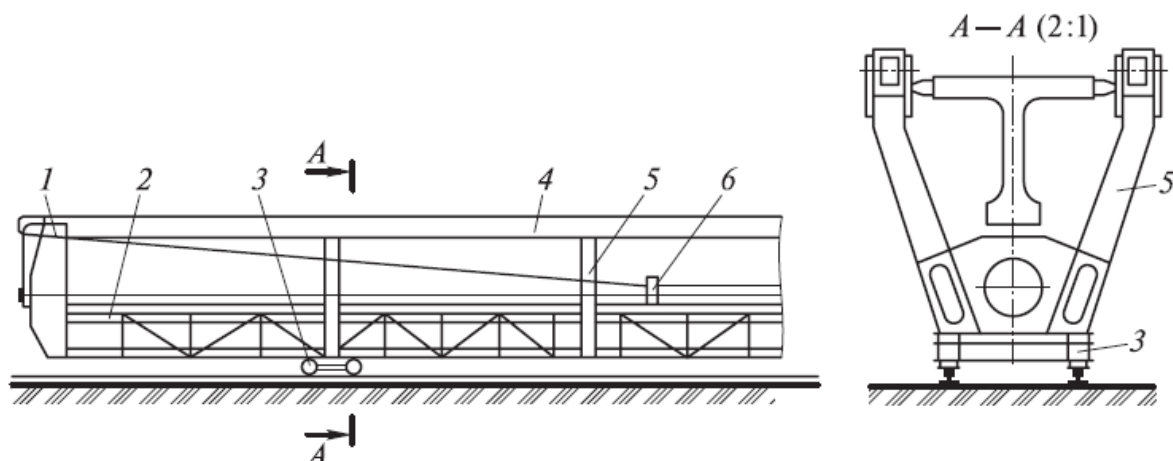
Схема передвижного стенда для изготовления предварительно напряженных балок:
